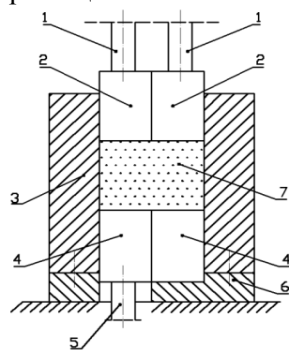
Схема пресс-формы для испытания цилиндрического образца:
